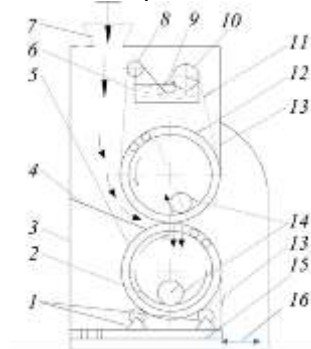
Схема устройства для приготовления модифицированного крахмала: 1 – роликовая опора; 2 – лоток; 3 – корпус; 4 – перегородка; 5 – ротор; 6 – ванна; 7 – загрузочный бункер; поз. 8 – опорный валик; 9 – прижимной валик; 10 – верхний опорный валик; 11 – сетка; 12 – прессующий вал; 13 – нож; 14 – разгрузочный шнек; 15 – платформа; 16 – отверстие.
